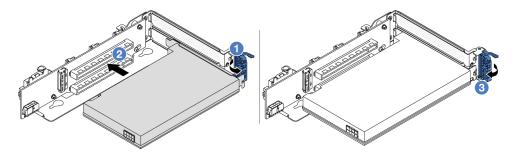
Установка адаптера PCIe в блок платы-адаптера Riser 3
